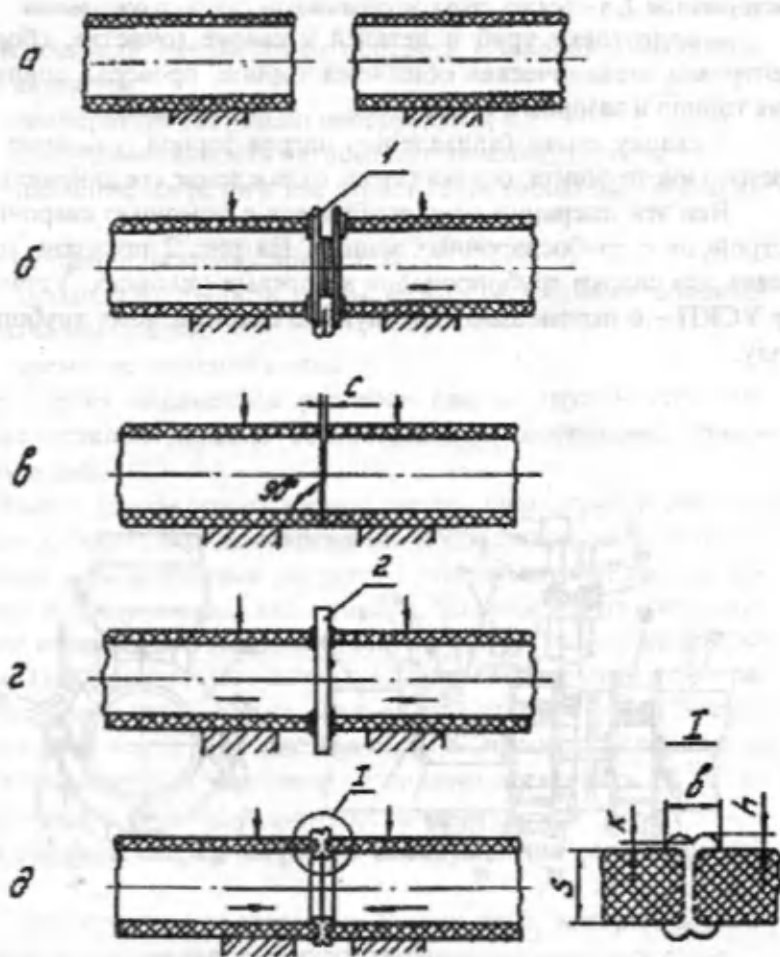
Последовательность процесса сборки и сварки встык труб из полистилена:
